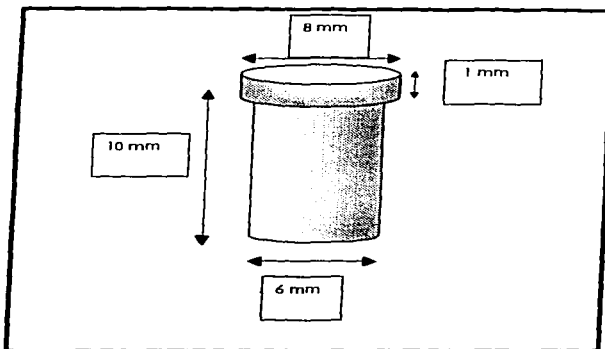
Forma y dimensiones de pieza maquinada de acero API X52
